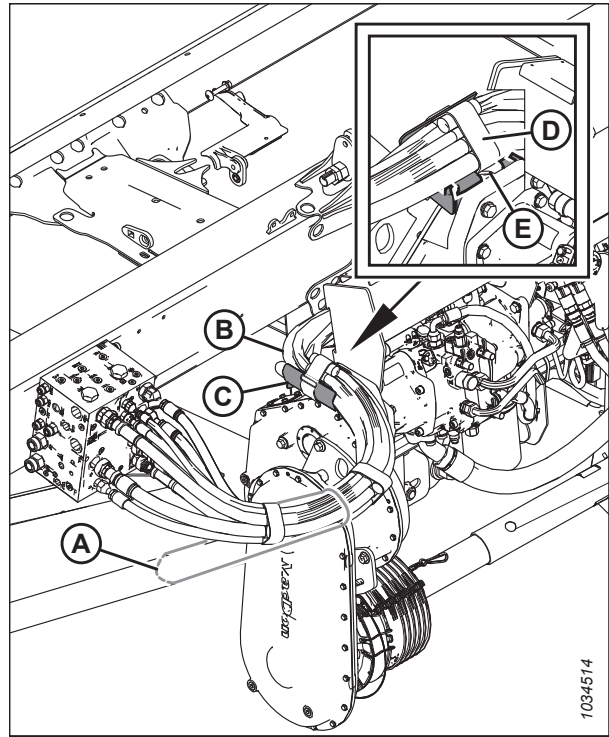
Flexibles hydrauliques – Configuration étroite
